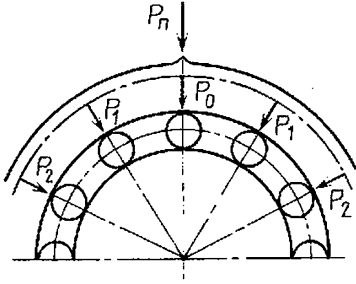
Расчетная схема нагружения роликоподшипника
